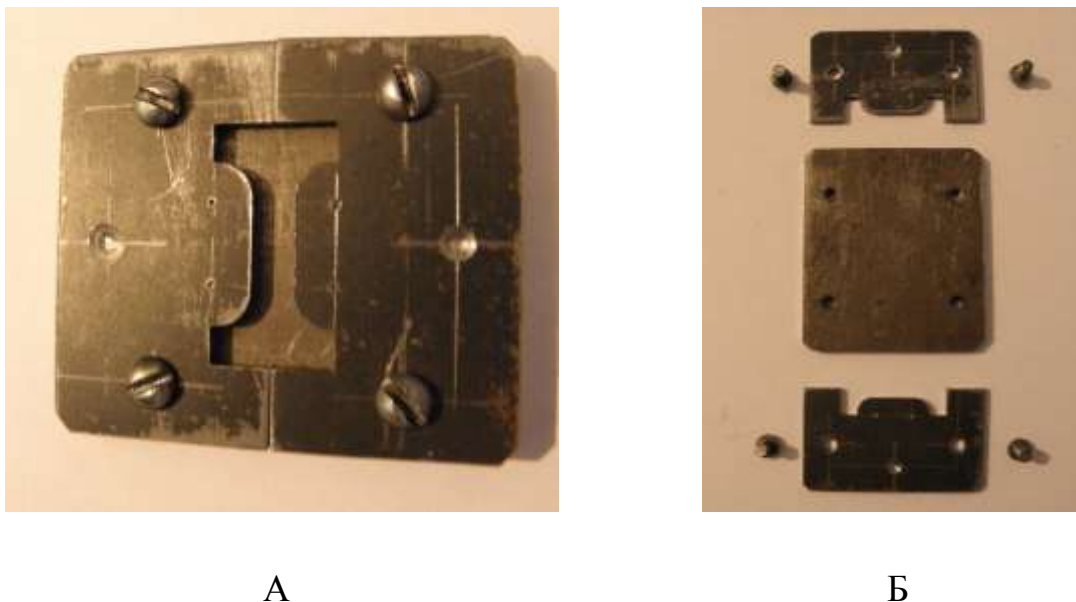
Вигляд металевої форми для виготовлення зразків на розтяг у зібраному (А) і розібраному стані (Б)
